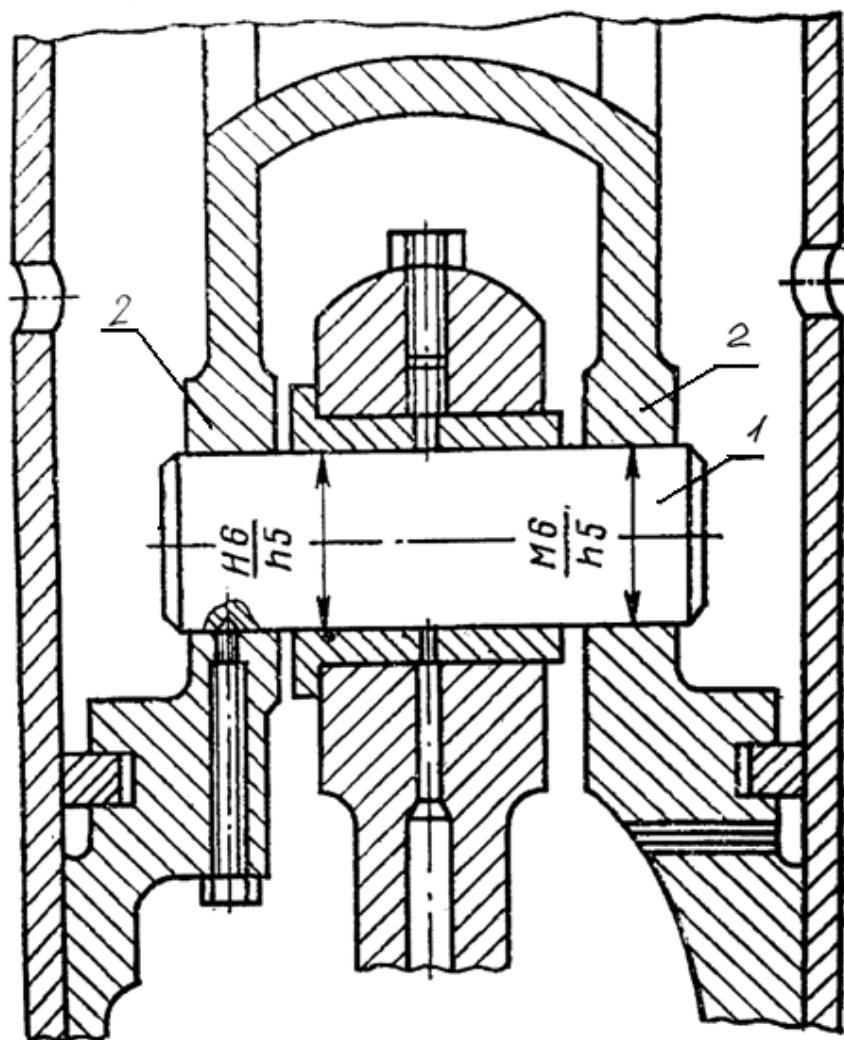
Посадка поршневого пальца-1 в бобышках-2 поршня компрессора
